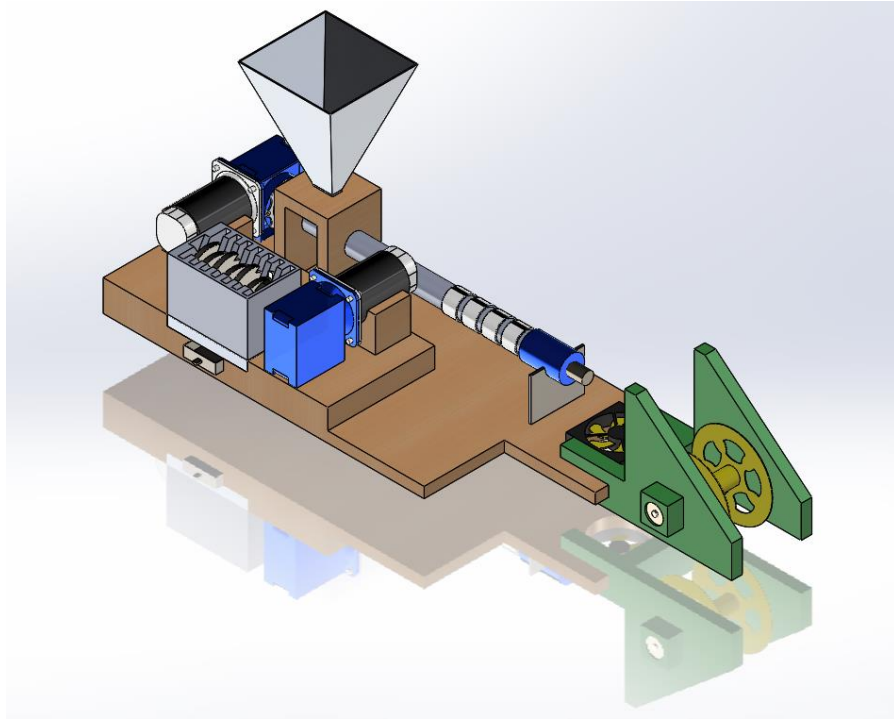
Ensamblaje final de la máquina extrusora vista 3
